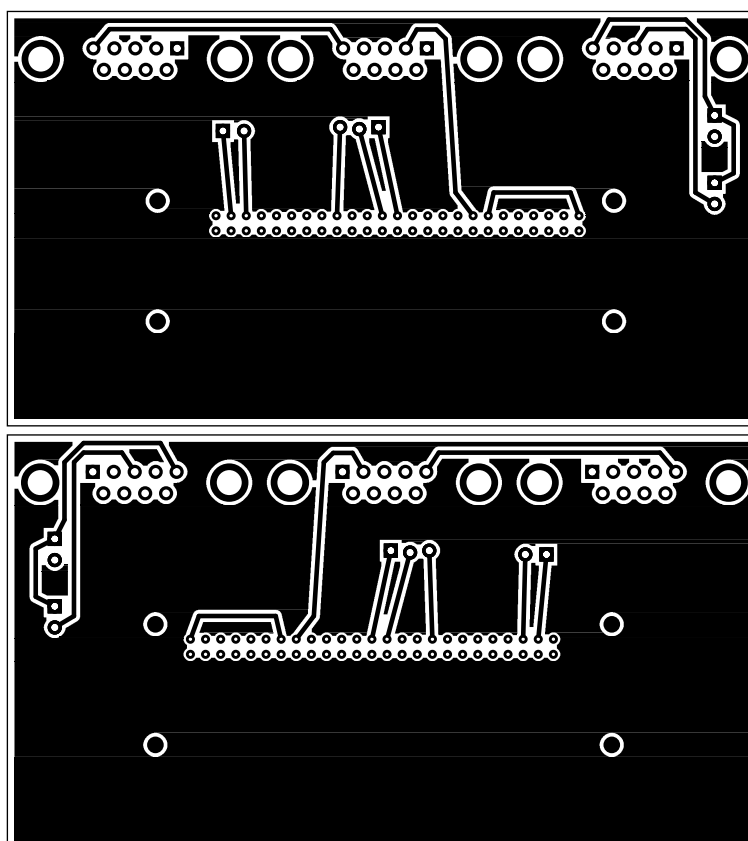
Circuito impresso da placa *Sensor Shield* em tamanho real. Parte inferior.
